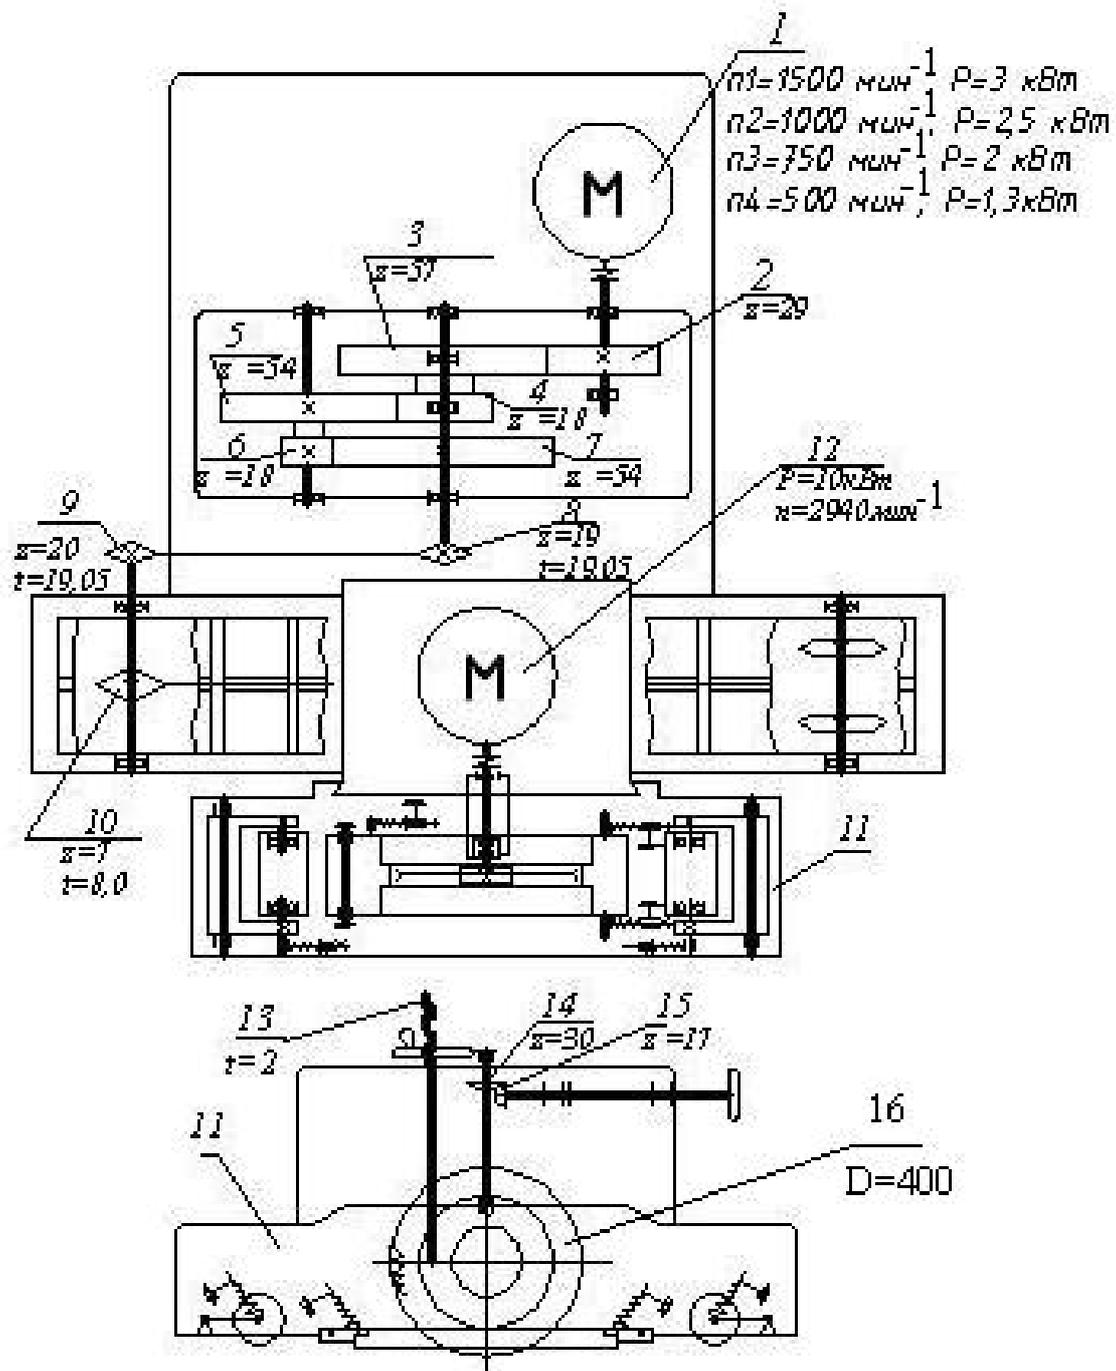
Кинематическая схема круглопильного станка с гусеничной подачей ЦДК-4
